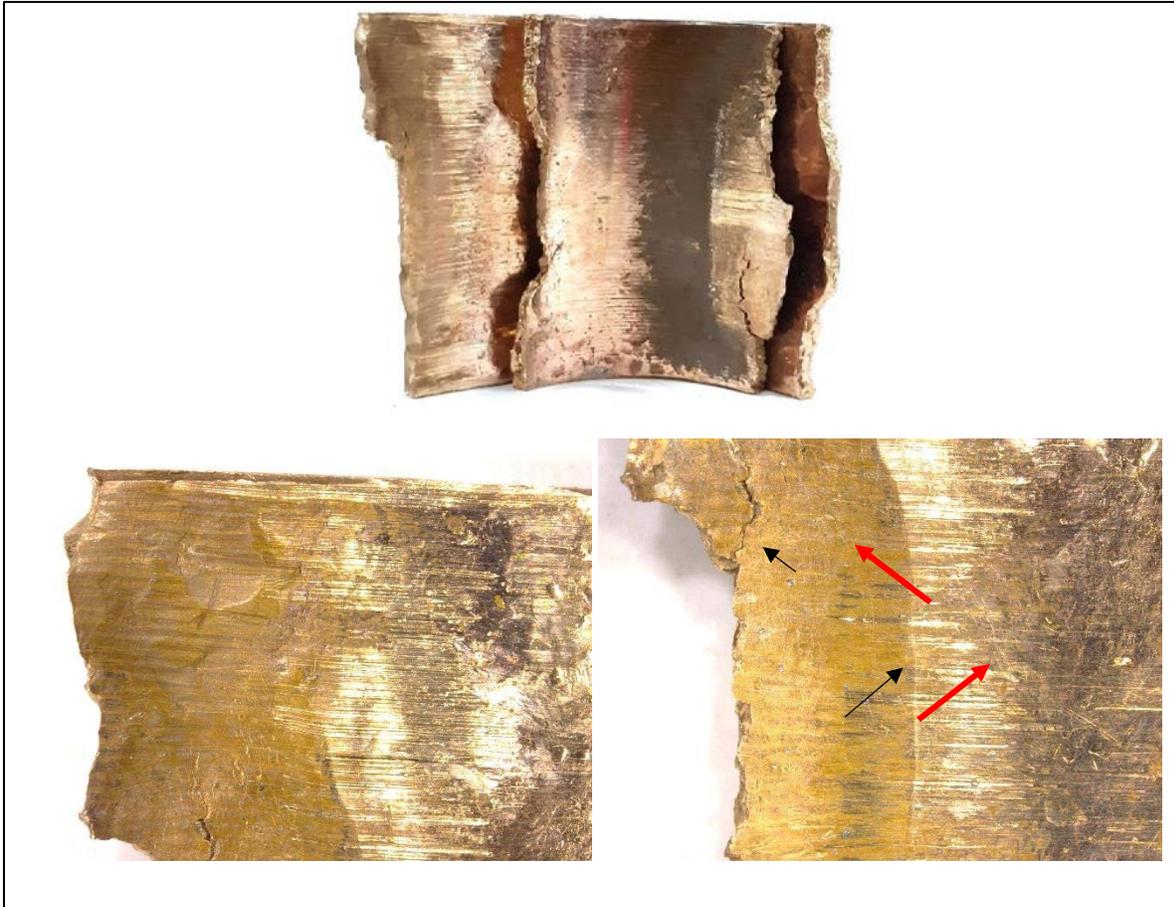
El buje presenta múltiples grietas longitudinales.
